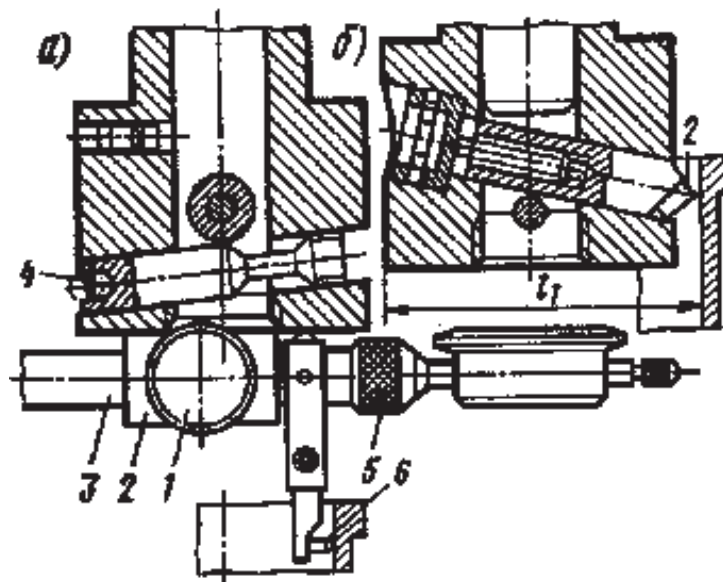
Різцева головка верстата 2А78Н з пристосуванням для центрування гільзи (а) і устанавлення різця (б)
